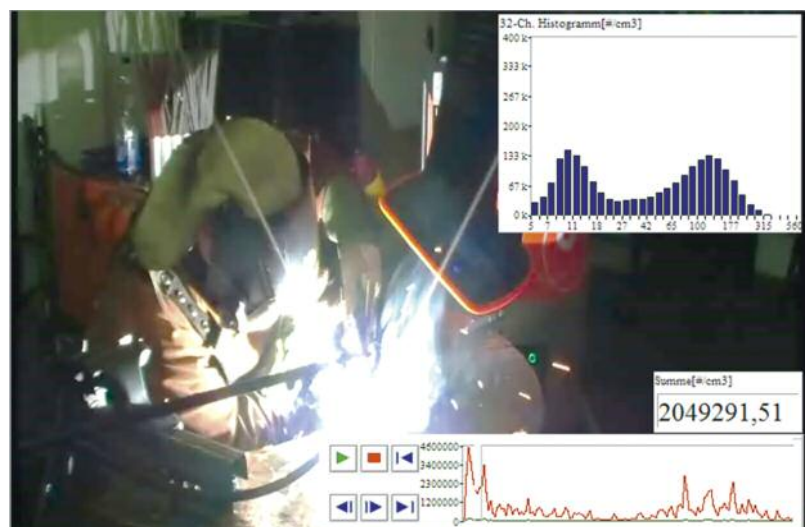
• Ausschnitt einer PIMEX-Observation (MAG-Schweißen mit Massivdrahtelektrode; Messsystem FMPS).
